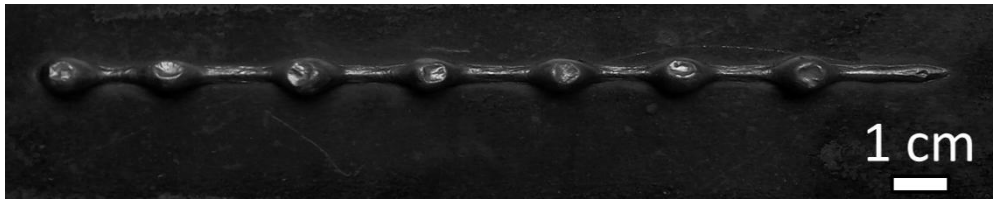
Exemple de dropping pour du soudage hybride en configuration arc laser
